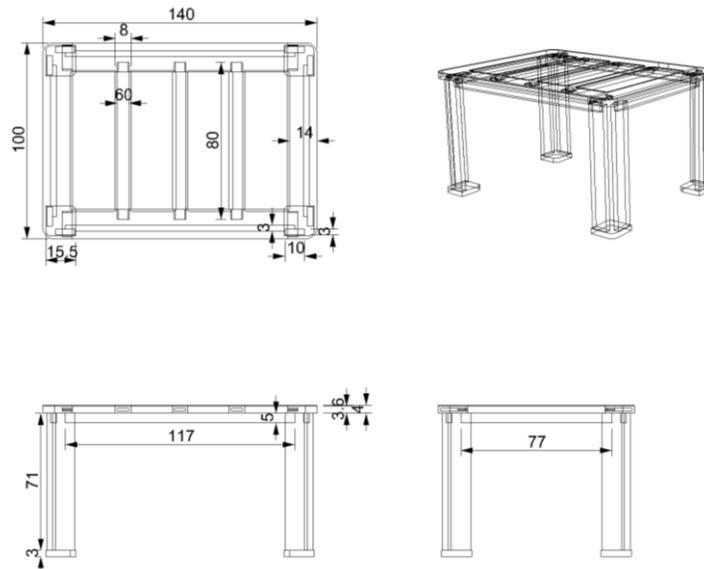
Antecedente Planos y Detalles Técnicos Mesa Comedor San Antonio
